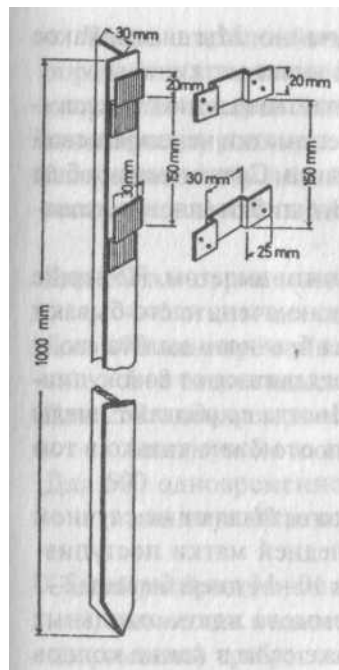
Сваи из профилированного (таврового) железа с крючками для крепления улейков позволяют легко устанавливать их почти на любой почве.
